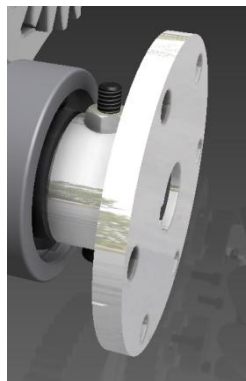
Ensamblaje del engranaje de acero del sistema Tri-Star
